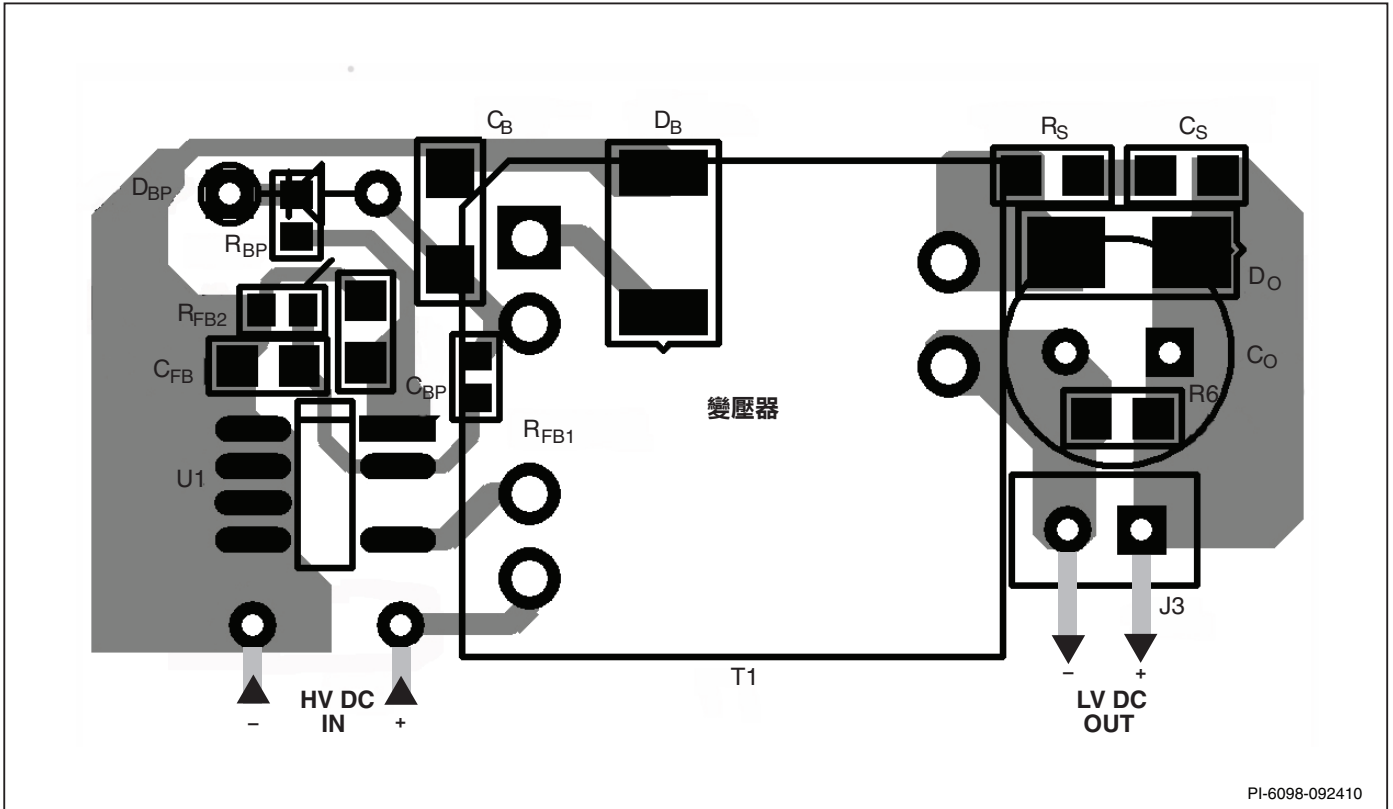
2.1 W、6 V、350 mA 充電器的 PCB 佈局。
